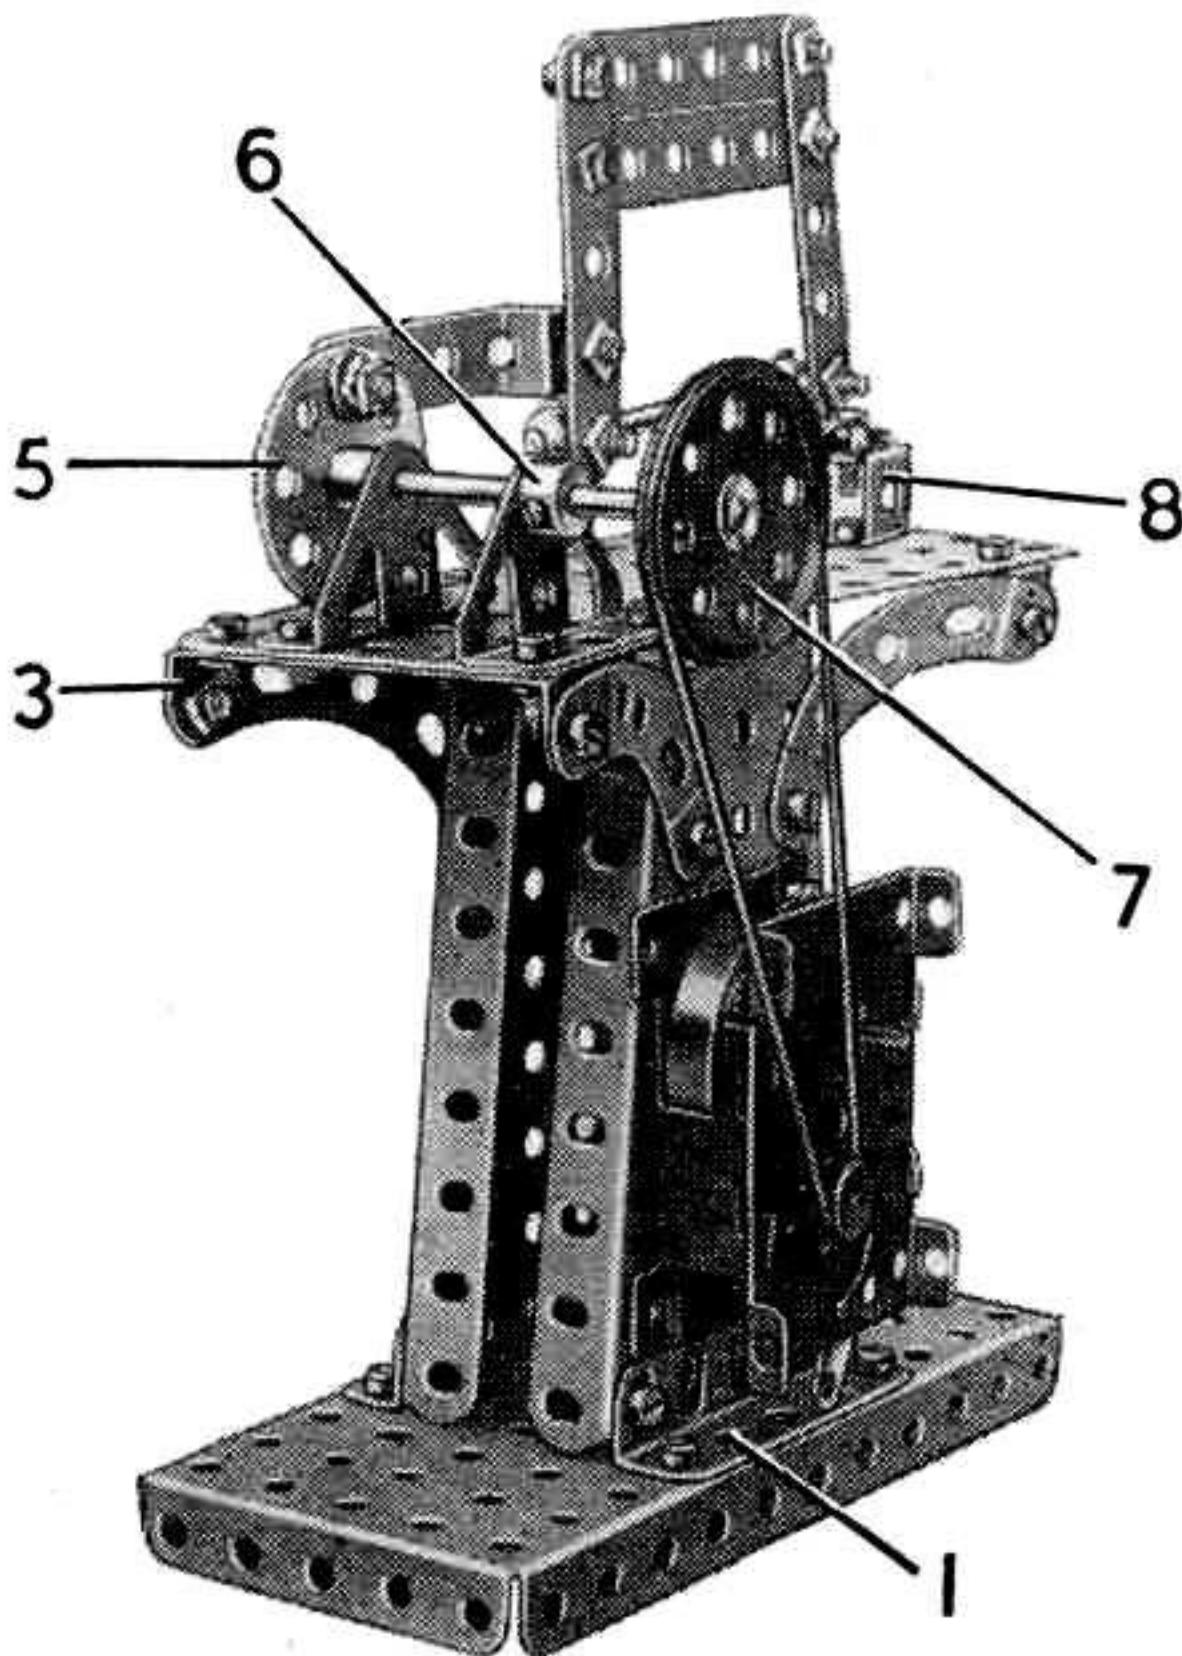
La scie à métaux vue de l'arrière avec la disposition du moteur et de l'entraînement.
